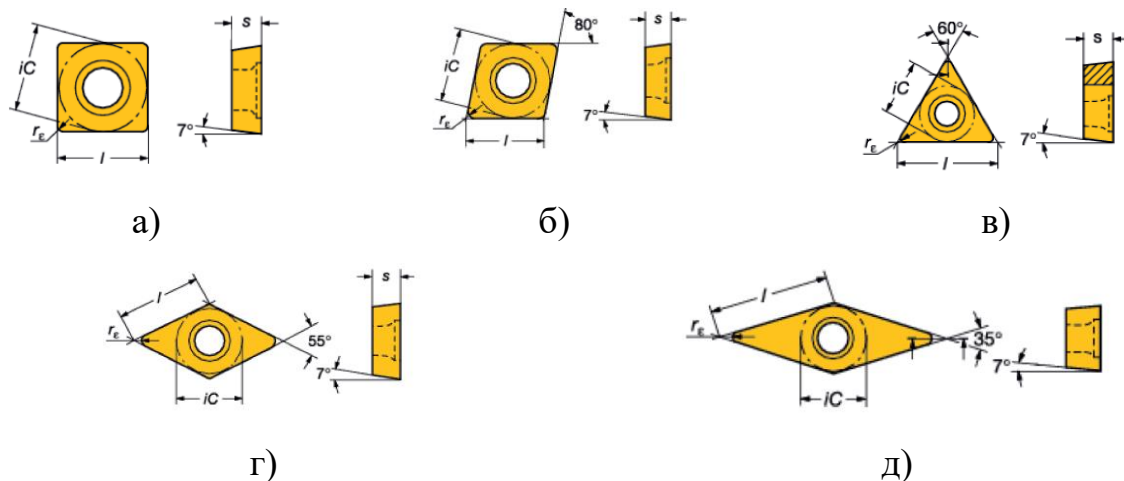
Різальні пластини для токарної обробки типу: а) SCMT; б) SSMT; в) TCMT; г) DCMT; д) VCMT
